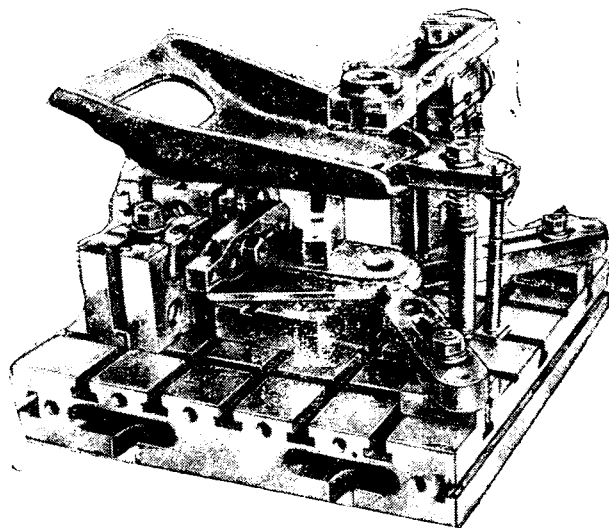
Кондуктор для сварного кронштейна.
